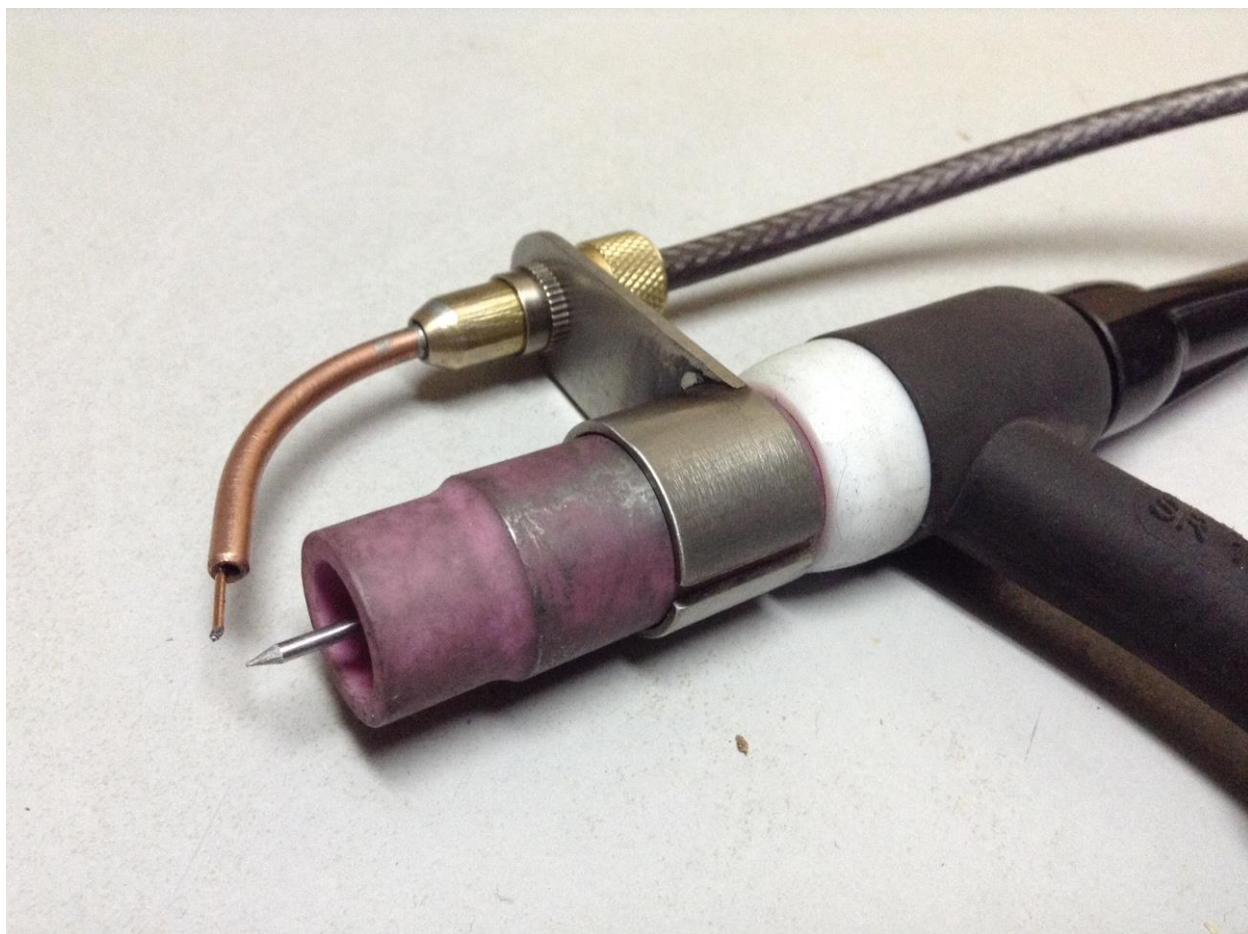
Горелка для механизированной сварки неплавящимся электродом
